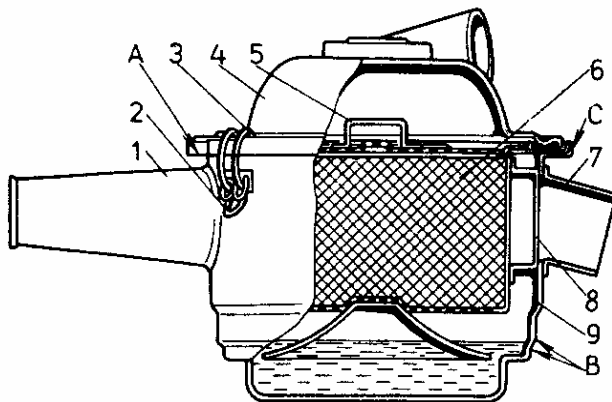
Depurador complementario de aire: 1 - tubuladura para tomar el aire frío; 2- palanca; 3- presilla; 4- tapa; 5 grapa; 6- elemento filtrante; 7- tubuladura para tomar el aire caliente; 8 - deflector; 9- cuerpo; A, B y C - marcas
